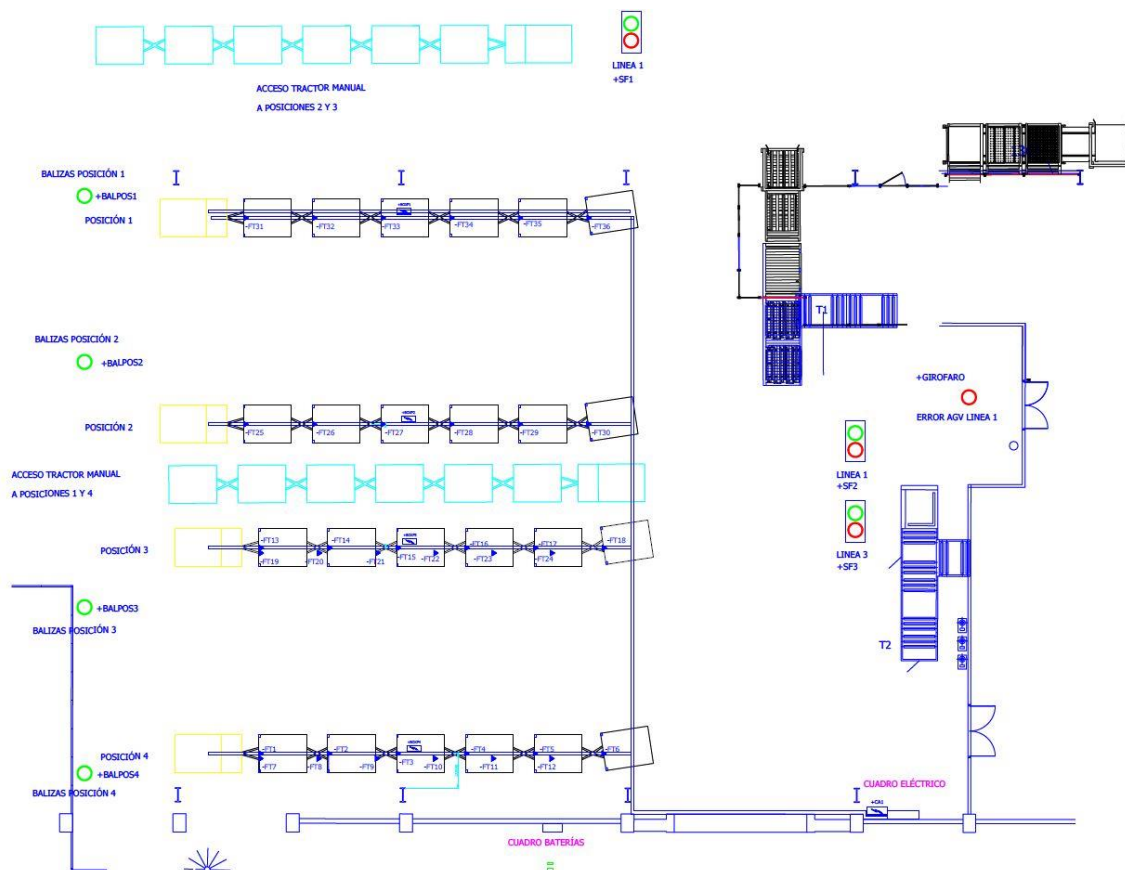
Ubicación de los elementos de campo en el Layout.
